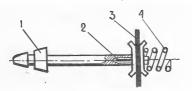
Отремонтированный шток: 1 — шток; 2 — винт M2,5; 3 — двафрагма; 4 — пружина.
